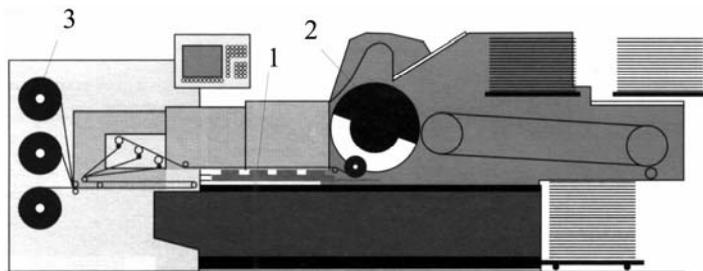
Схема плоскопечатного пресса для тиснения фольгой PZ 90 фирмы Stauer: *1* — плитка; *2* — цилиндр; *3* — фольговый аппарат
